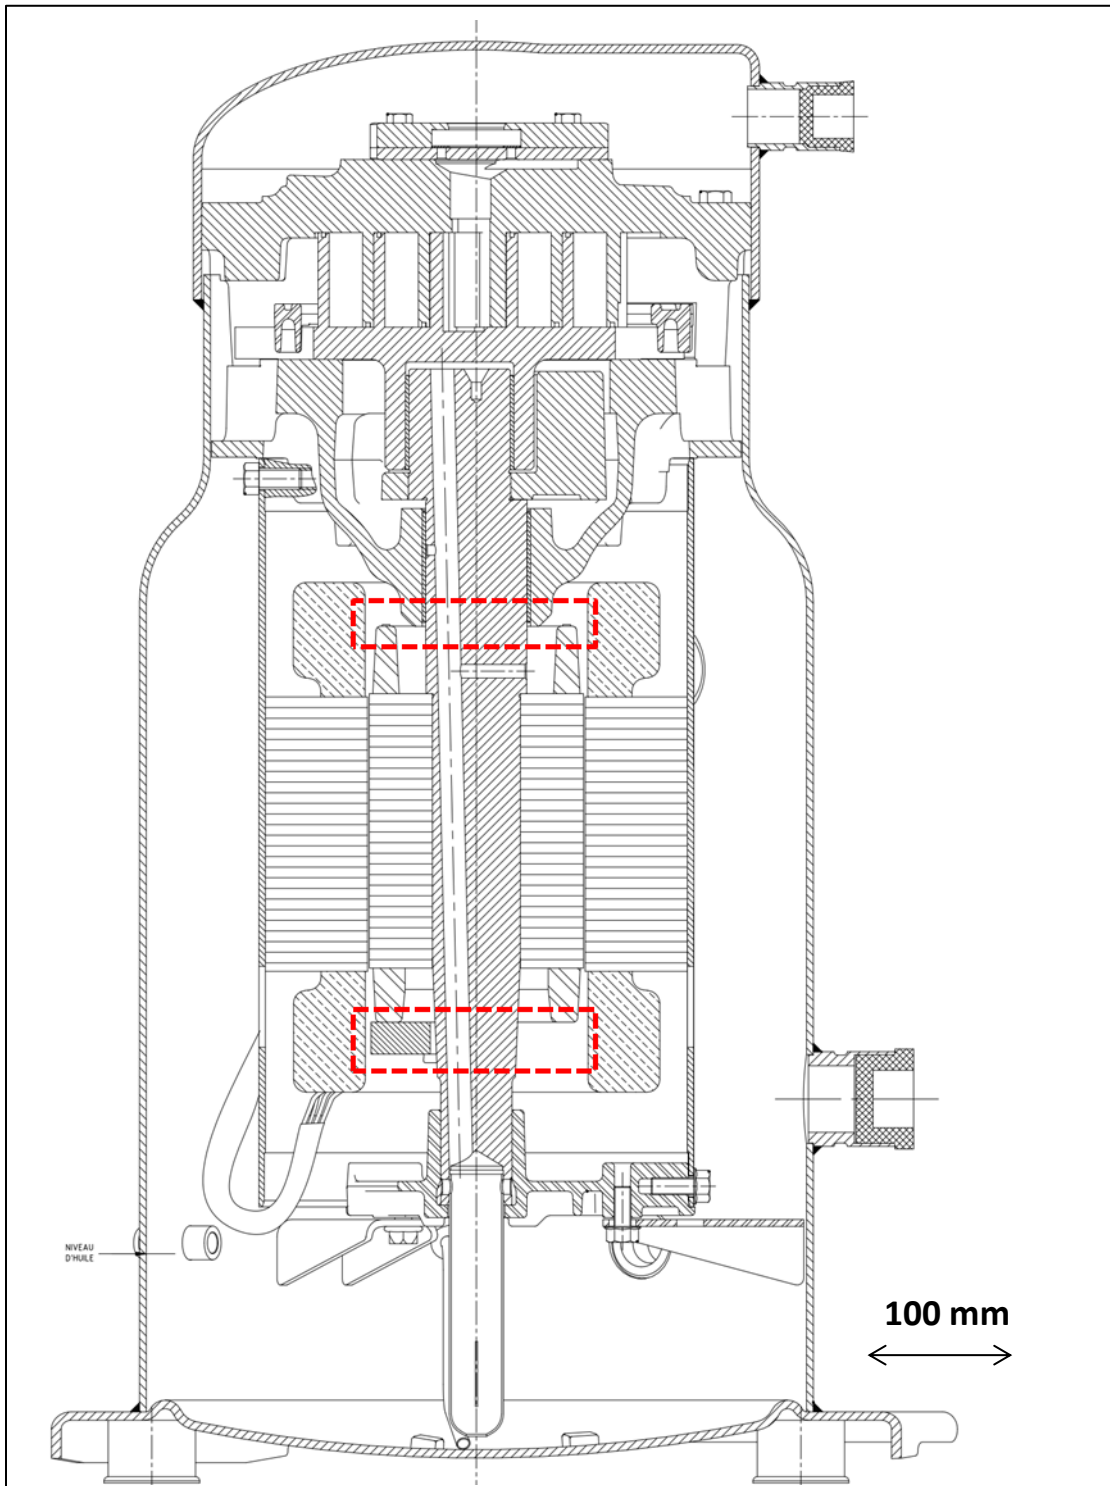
Dessin d'ensemble du compresseur. Les zones d'intégration des masselottes sur le rotor sont repérées par les cadres rouges pointillés
